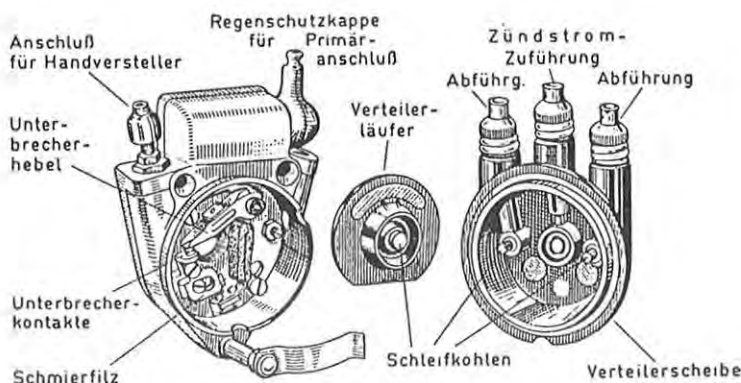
Innenansicht des Bosch-Zündunterbrechers mit Verteiler für Zweizylindermotoren
